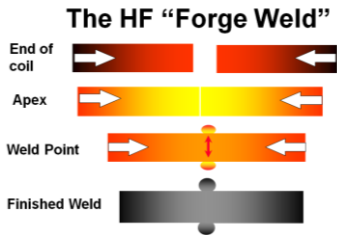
foto de soldadura cedida por flinsa
